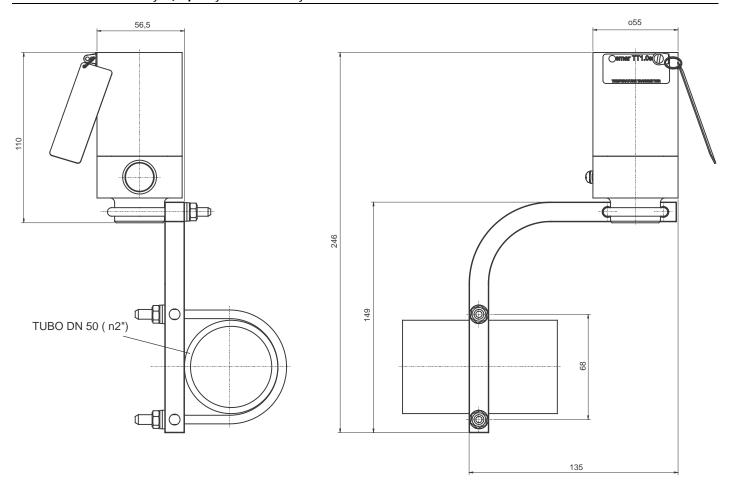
Desenho Dimensional e Posições de Montagem – Modelo Sem Visor
